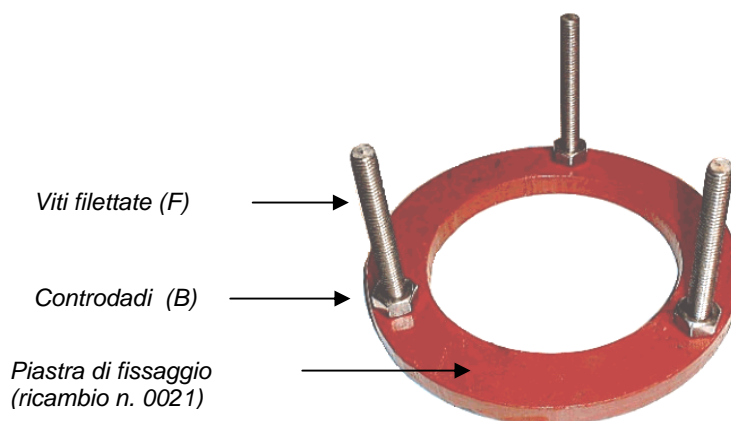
Piastra di fissaggio preparata per attacco all'anello di serraggio
